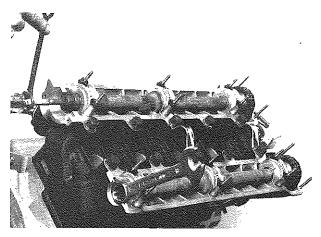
Ruotare gli assi a camme Rotating camshafts
